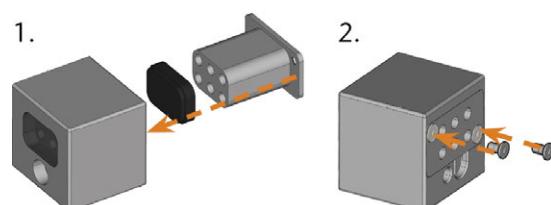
COLOCAR UN INSERTO EN UN ALMACÉN DE HERRAMIENTAS
